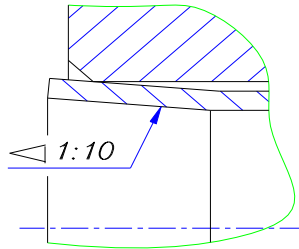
Конічне розвальцьовування труби перед зварюванням
